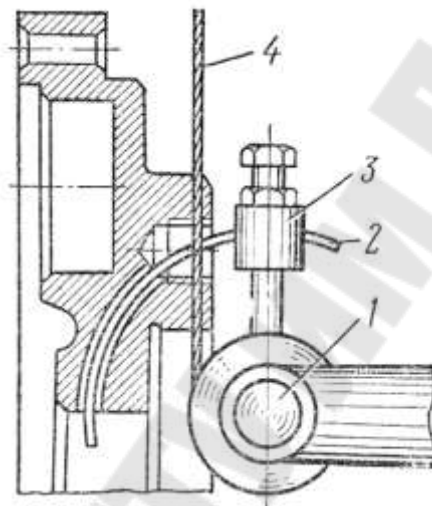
Схема прошивки отверстий с криволинейной осью
